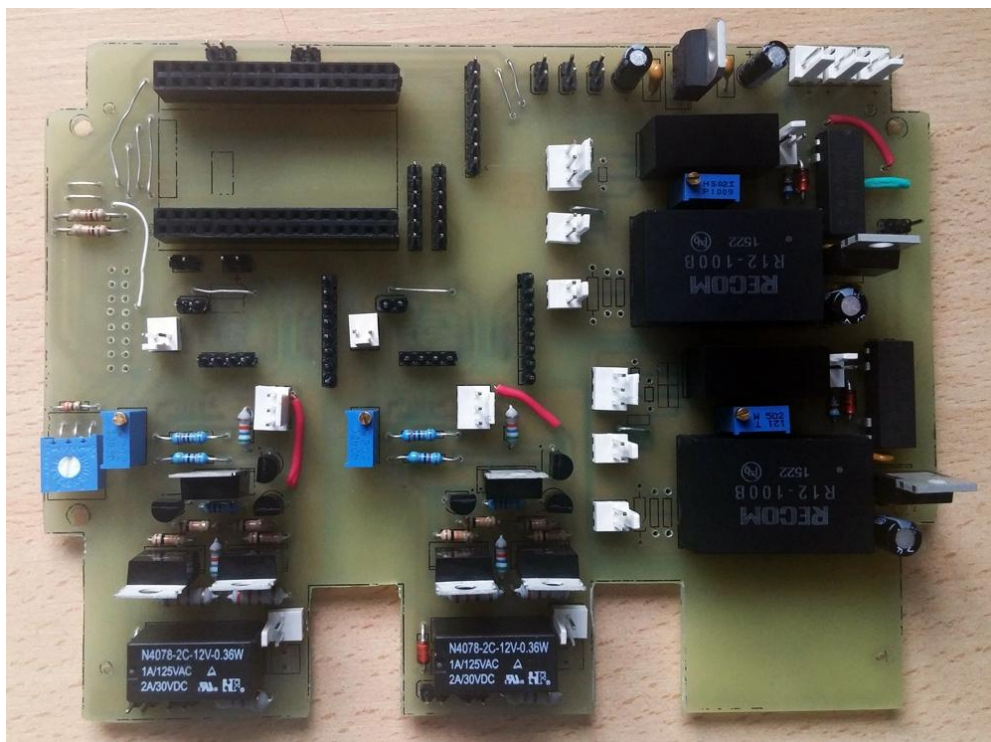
Placa principal con todos sus componentes soldados.
